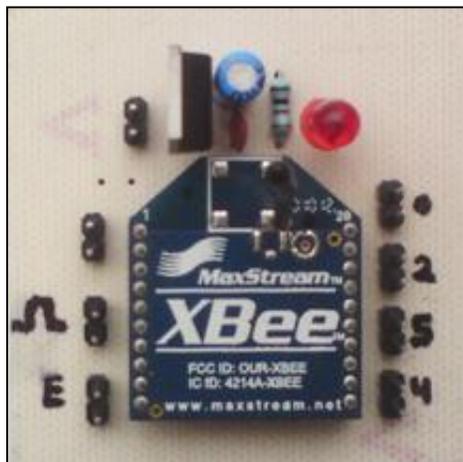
a) PCB de Modulo XBee con componentes electrónicos.
